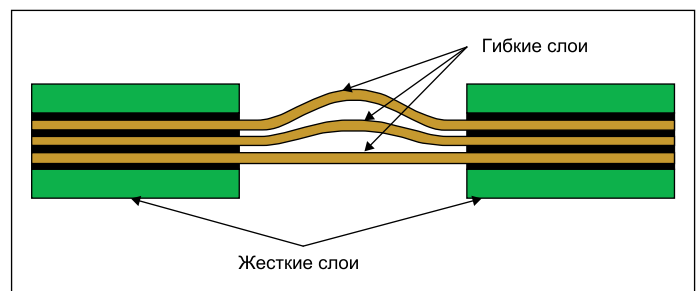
Конструкция печатной платы с воздушными зазорами между гибкими слоями
